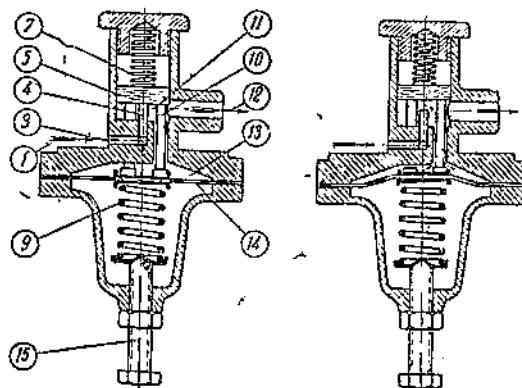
Принципиальная схема редуктора высокого давления для сжиженного газа
